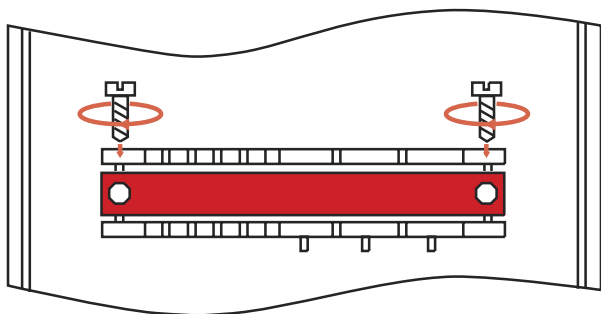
Крепление кабелей с помощью специальной монтажной планки.
